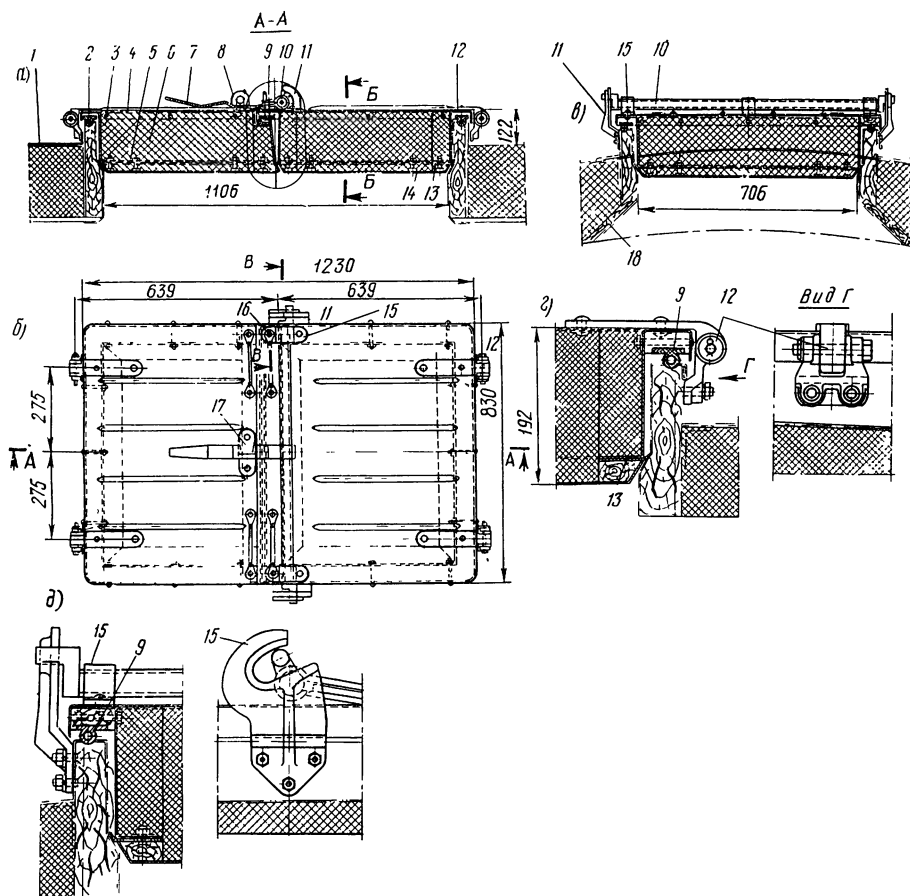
Устройство льдозагрузочного люка вагонов-ледников конструкции 1956 г.: а — продольный разрез; б — план; в — поперечный разрез; г — крепление петли, д — крепление кронштейнов кривошипного запора; 1 — металлическая обшивка крыши; 2 — деревянная рама горловины люка; 3 — алюминиевая коробка с вырезом в днище; 4 — верхняя крышка коробки из гофрированного алюминия толщиной 2 мм; 5 — днище крышки, выполненное из оцинкованной стали; 6 — теплоизоляция (мипора в пакетах); 7 — ручка запора; 8 — ушко; 9 — резиновая трубка; 10 — стержень затвора; 11 — кронштейн запора с гнездом для кривошипа; 12 — петля крышки; 13 — полосовая резина; 14 — болт, скрепляющий резину между деревянным брусом и стенкой коробки; 15 — кольцо запора; 16 — ручка крышки; 17 — откидное ушко; 18 — скос в горловине люка для удобства загрузки льда в баки
